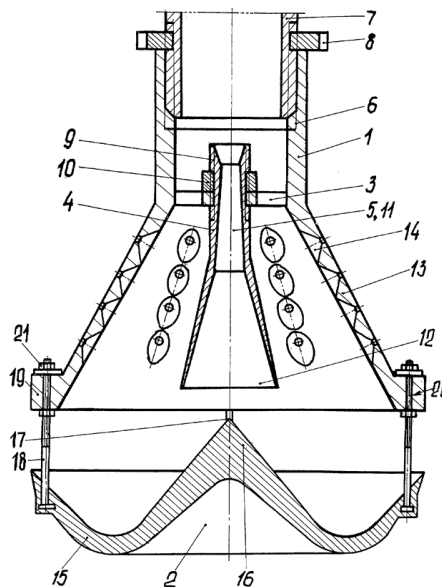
Насадок дождевального агрегата с нижним расположением дефлектора.
